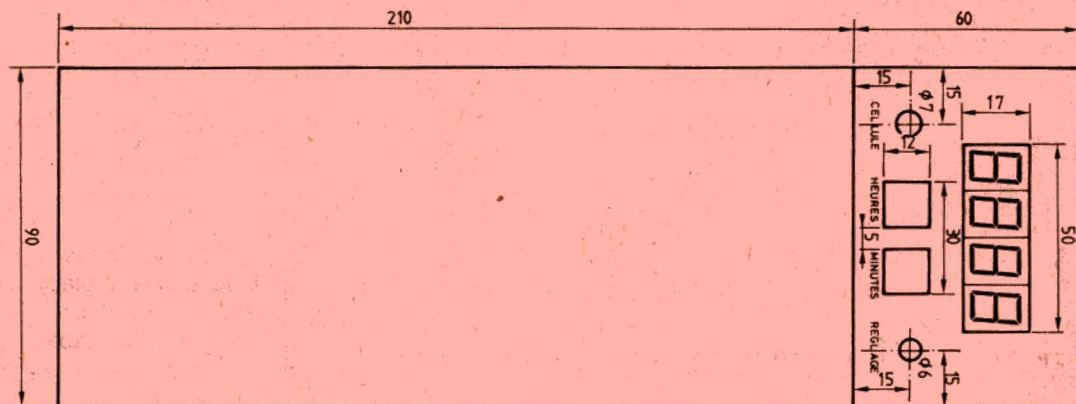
Proposition pour une mise en coffret. Sa façade réduite permet de trouver facilement une place sur ou sous le tableau de bord.
